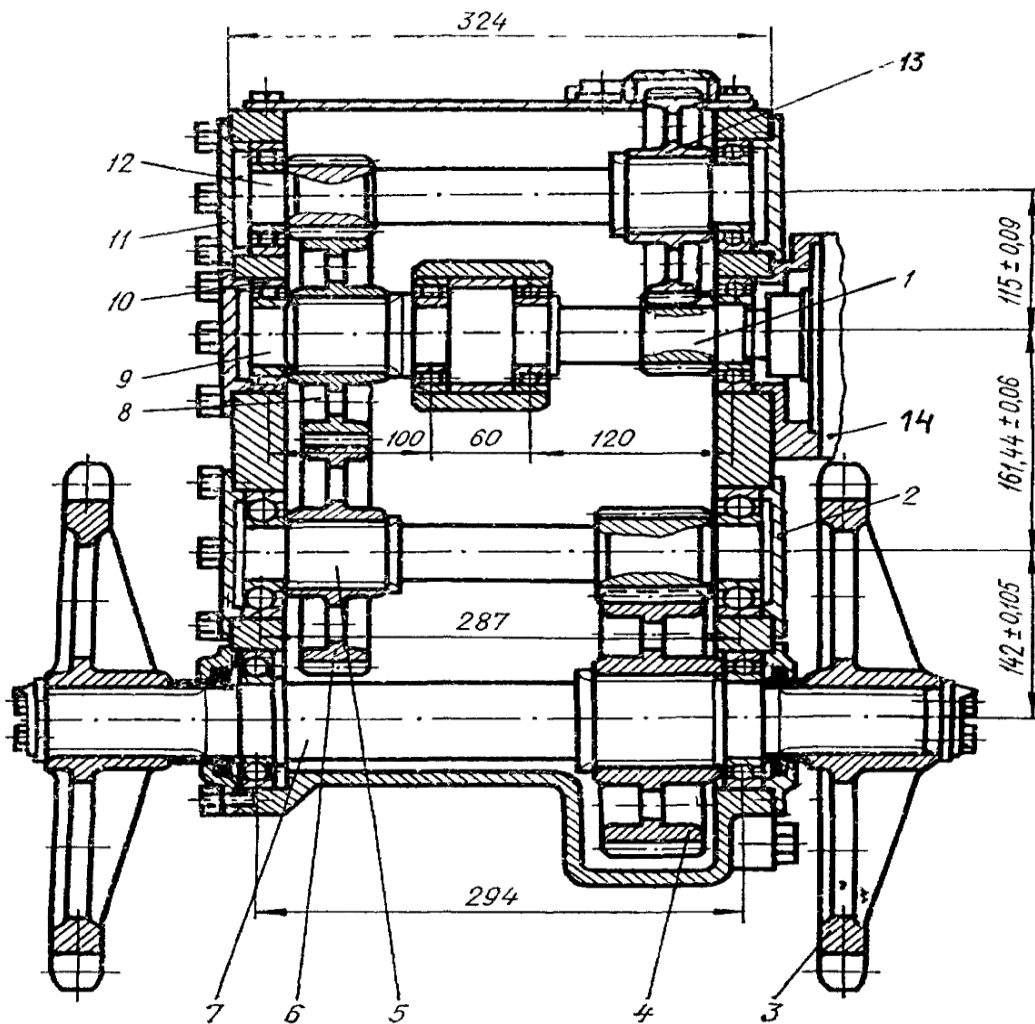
Редуктор привода ковшовой цепи каналоочистителя:
